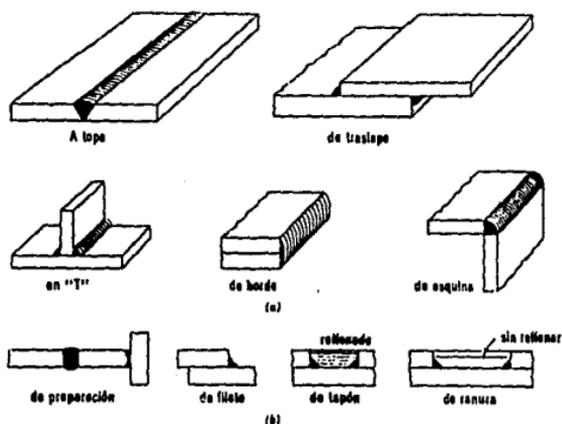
Conexiones Soldadas: (a) Tipos de Juntas, (b) Tipos de Soldaduras.
